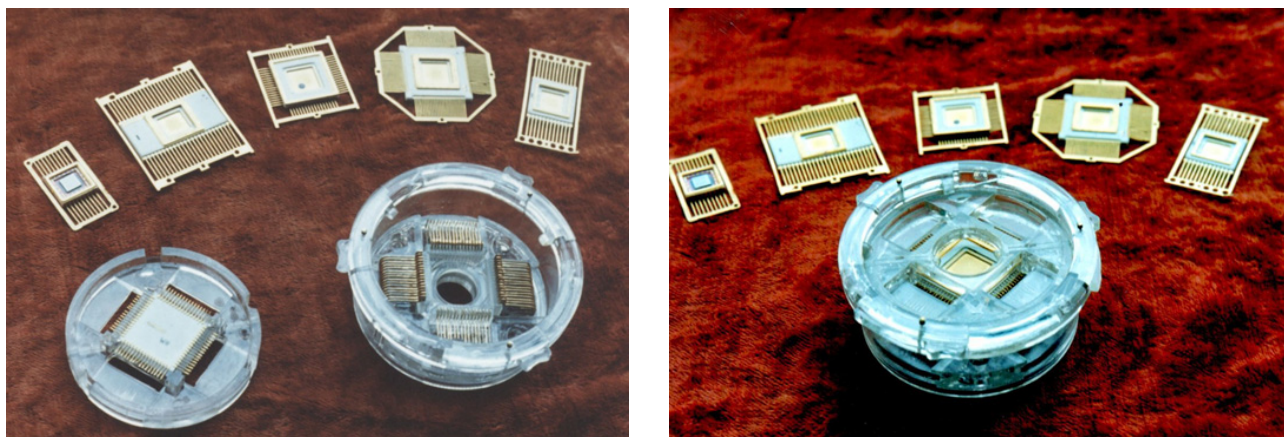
Прецизионные детали и приспособления для производства изделий микроэлектроники
